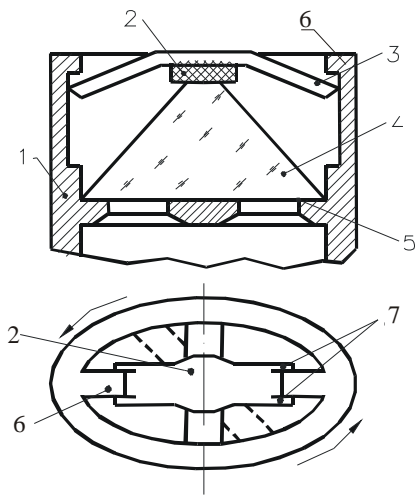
Кріплення призми БР-180⁰ у корпусі: 1 – корпус; 2 – еластична прокладка; 3 – пружинна планка; 4 – призма; 5 – упор в оправі; 6 – виступ на оправі; 7 – лапки
